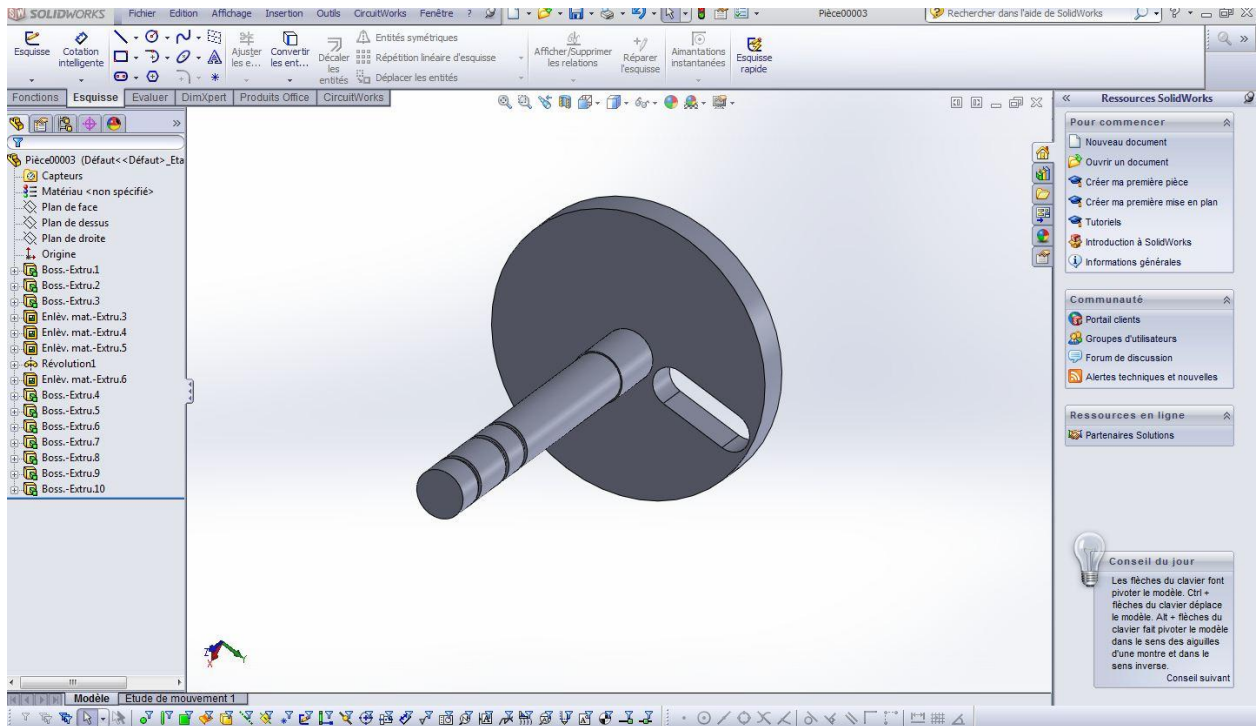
Vue Disque et arbre rotatif réalisée sous SOLIDWORKS
